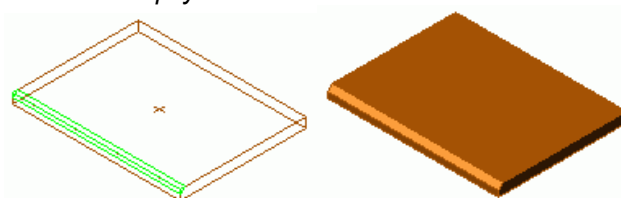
Пластина с разделкой кромки под сварку
